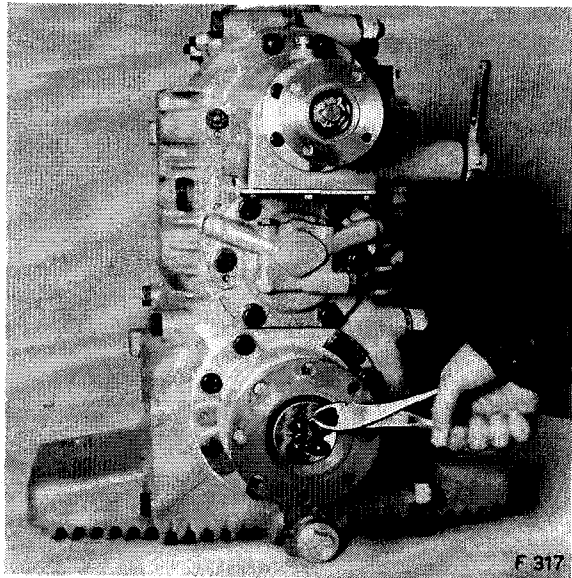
Lösen der Schrauben des hintern Aufhängesupports rechts (gleich wie links)
